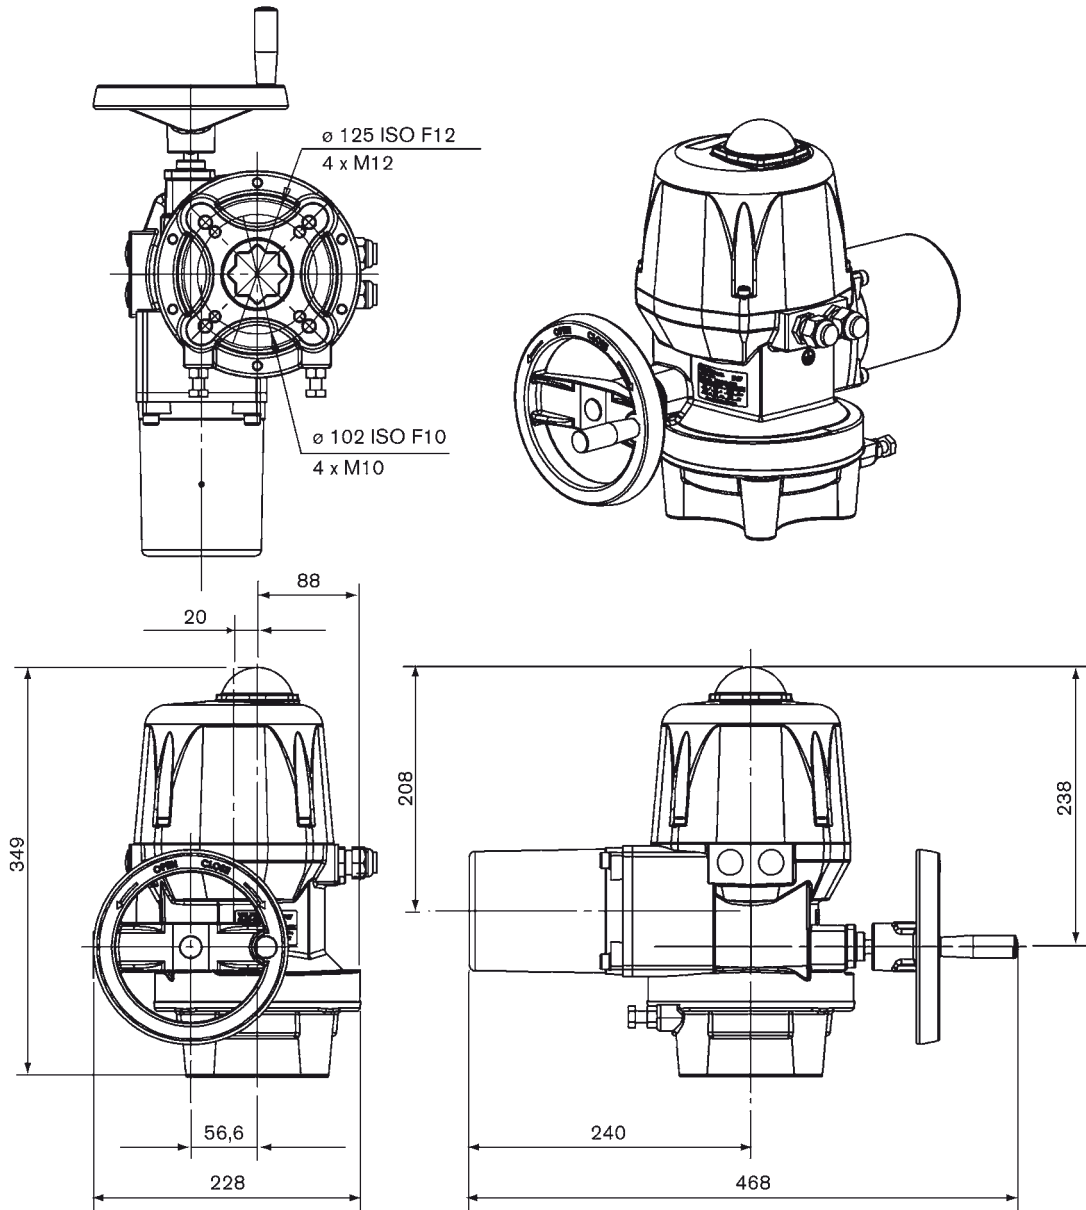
Dimensions type 3005 avec couple de serrage 600 - 1 000 Nm
